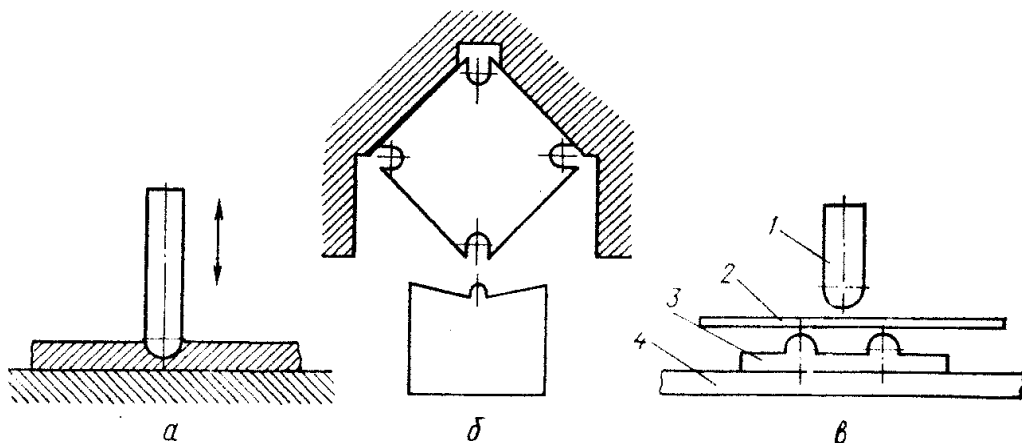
Периодические способы рилевки: а – рилевка ножом против плоской подкладки; б – рилевка ножом против паза; в – рилевка рабочей линейкой против матрицы: 1 – рабочая линейка; 2 – материал; 3 – матрица; 4 – подкладка
